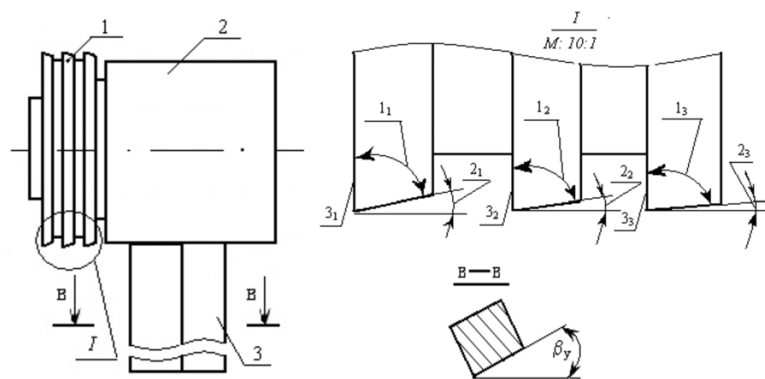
Ротационный режущий инструмент: 1 – режущие элементы; 2 – корпус; 3 – державка
